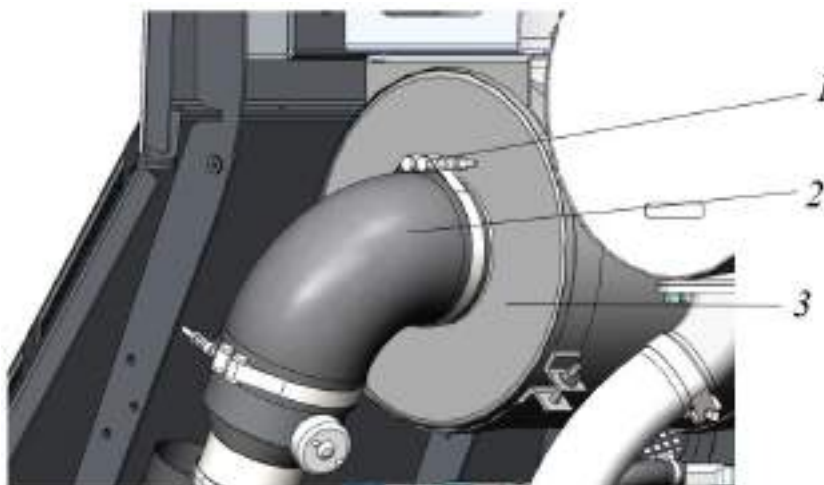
Демонтаж патрубка корпуса воздушного фильтра
